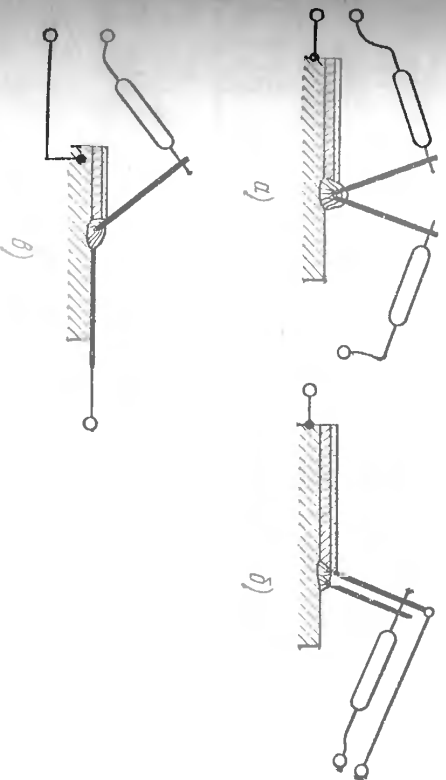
Способы сварки трехфазной дугой: а — двумя держателями, б — параллельными электродами, в — электродом, уложенным на заготовку
